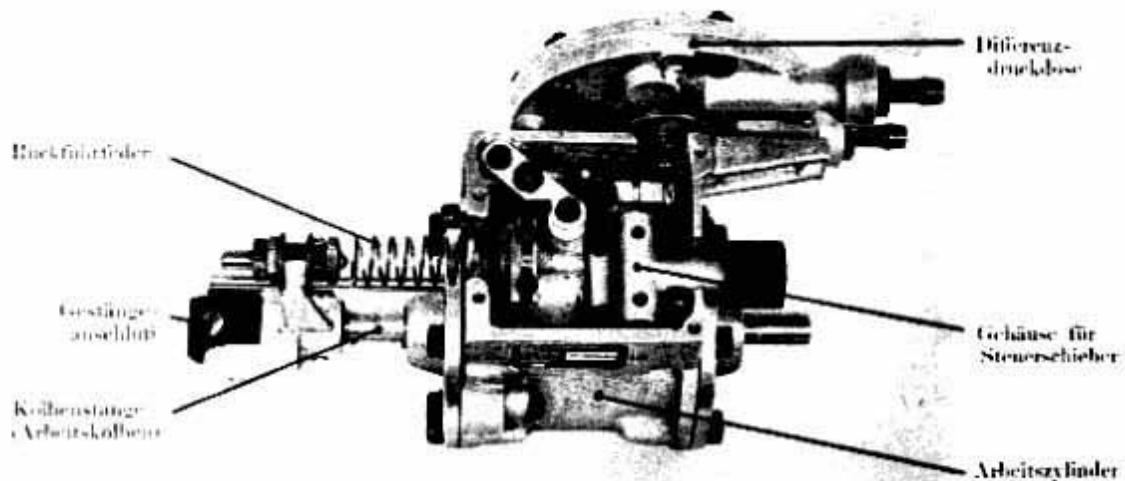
Rudermaschine. Ansicht schräg von oben, Deckel abgeschraubt
